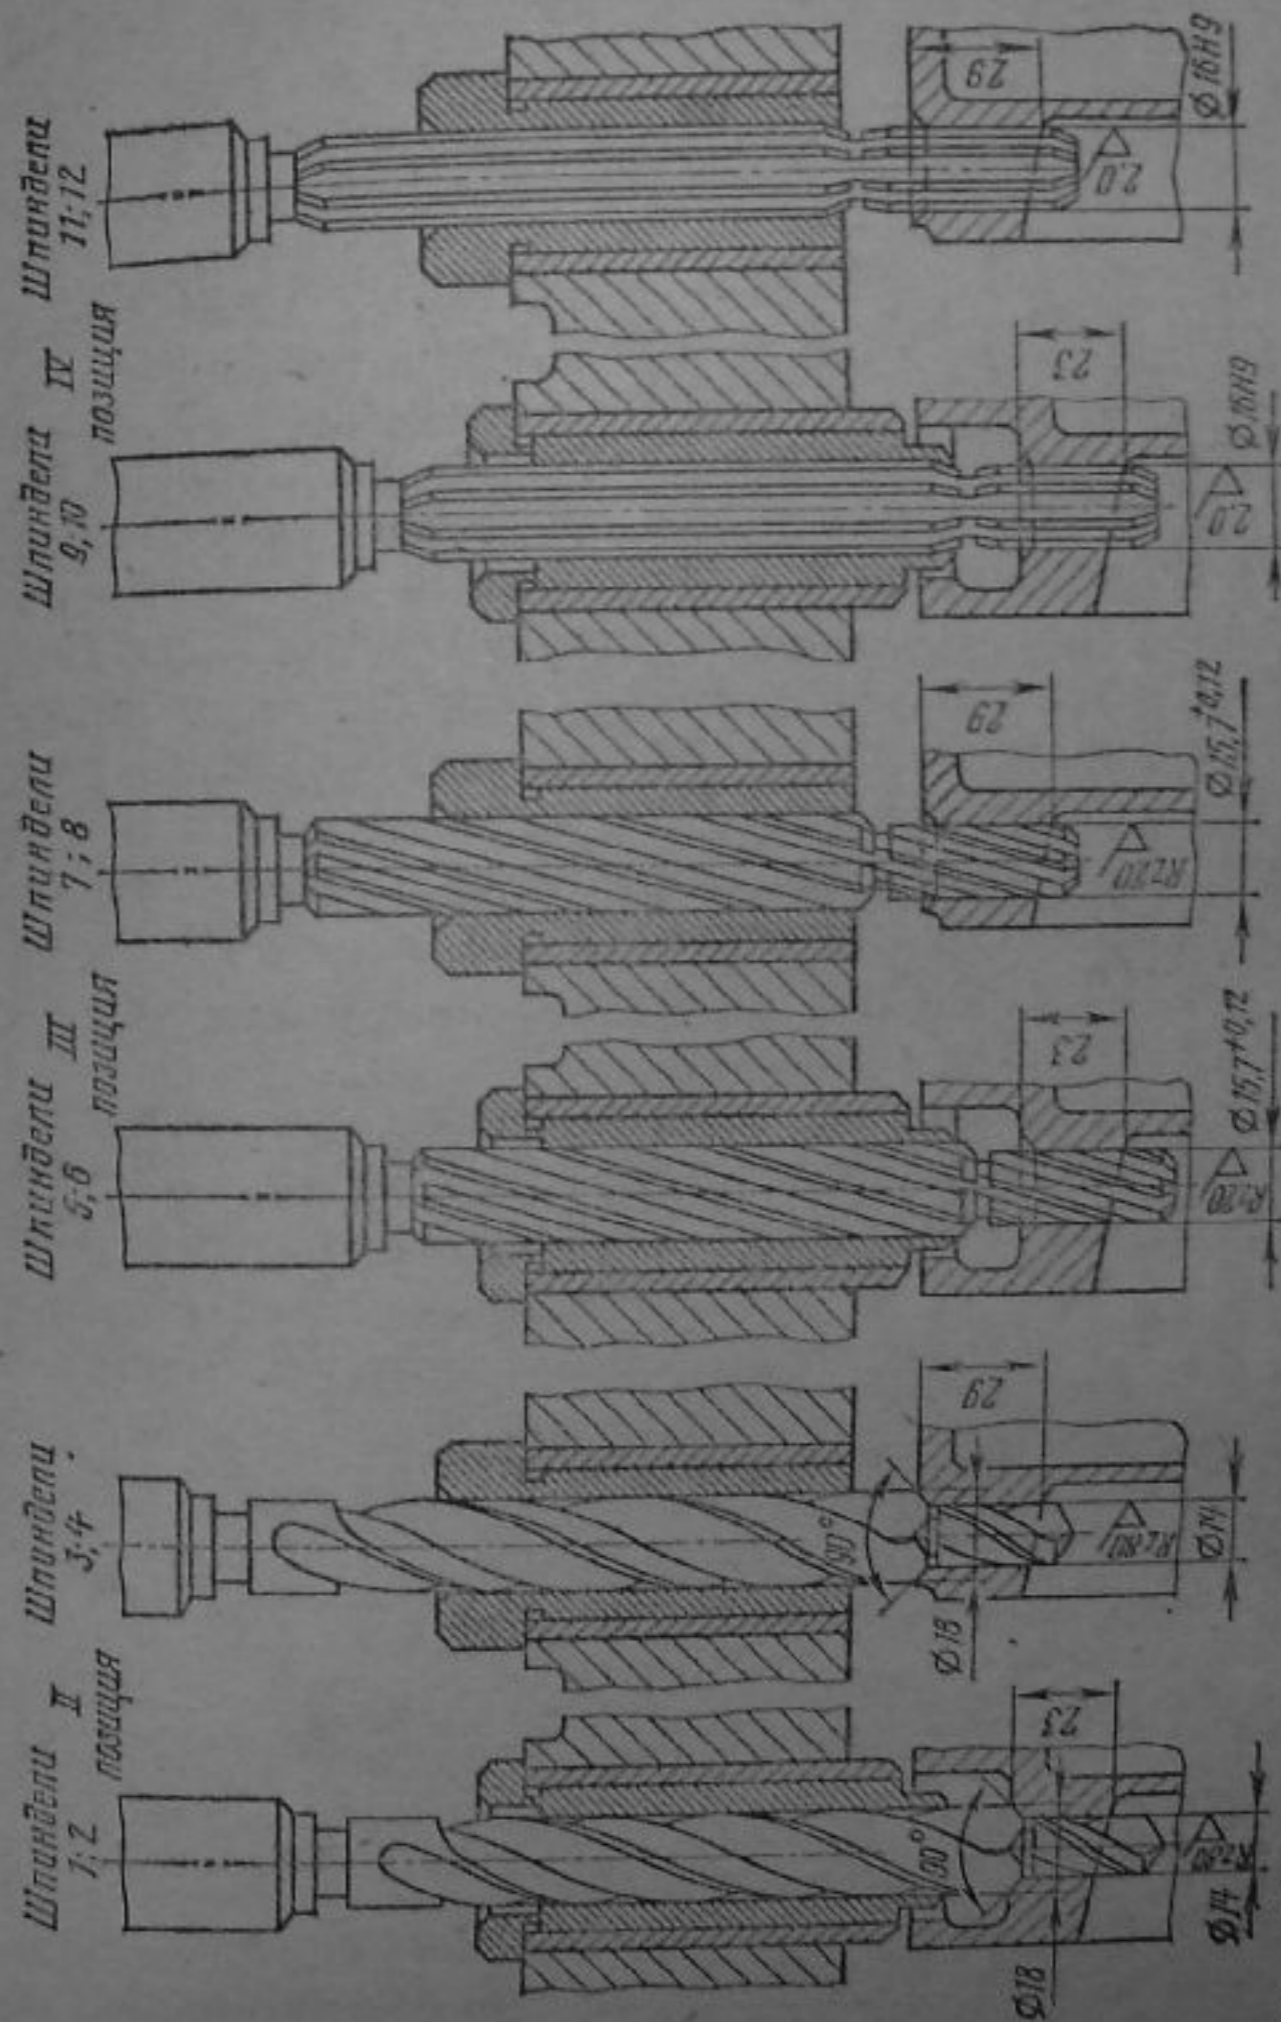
Эскиз наладки 12-шпиндельного агрегатного вертикально-сверлильного станка для обработки корпуса: позиция I — сверление четырех отверстий  $\varnothing 14$  мм с зенкованием фасок под углом  $90^\circ$  до  $\varnothing 18$  мм; позиция II — зенкование четырех отверстий  $\varnothing 15,7^{+0,12}$  мм; позиция III — развертывание четырех отверстий  $\varnothing 16H9$
